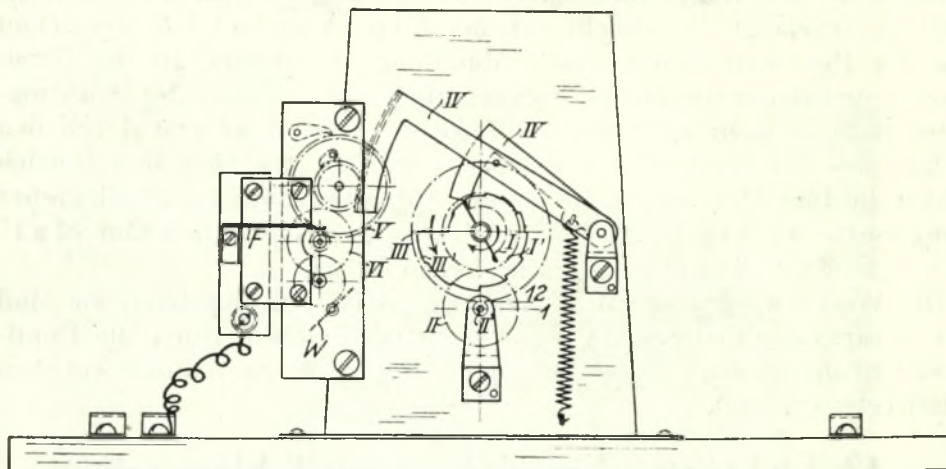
Hammersteuerung der Möller-Uhr mit Schlagwerk
